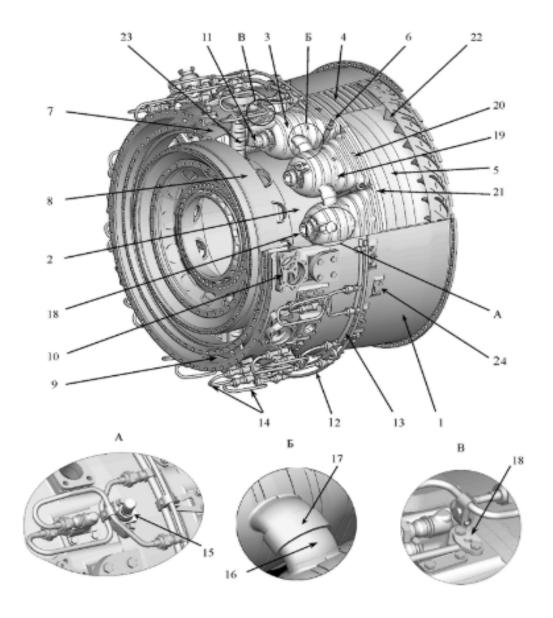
Трубчато-кольцевая КС: 1 — наружный корпус КС; 2 — внутренний корпус КС; 3 — жаровая труба; 4 — наружное кольцо газосборника; 5 — внутреннее кольцо газосборника; 6 — силовая стойка; 7 — наружное кольцо диффузора; 8 — внутреннее кольцо диффузора; 9 — полость отборов воздуха; 10 — фланцы отбора воздуха; 11 — форсунка; 12 — топливный коллектор первого контура; 13 — топливный коллектор второго контура; 14 — трубопроводы подвода топлива к форсунке; 15 — свечи зажигания; 16 — пламеперебрасывающий патрубок; 17 — пламеперебрасывающая муфта; 18 — подвеска жаровой трубы; 19 — отверстия первичной зоны; 20 — отверстия зоны смешения; 21 — рамочный фланец жаровой трубы; 22 — сопловой аппарат ТВД; 23 — перепускная труба; 24 — лючок осмотра
